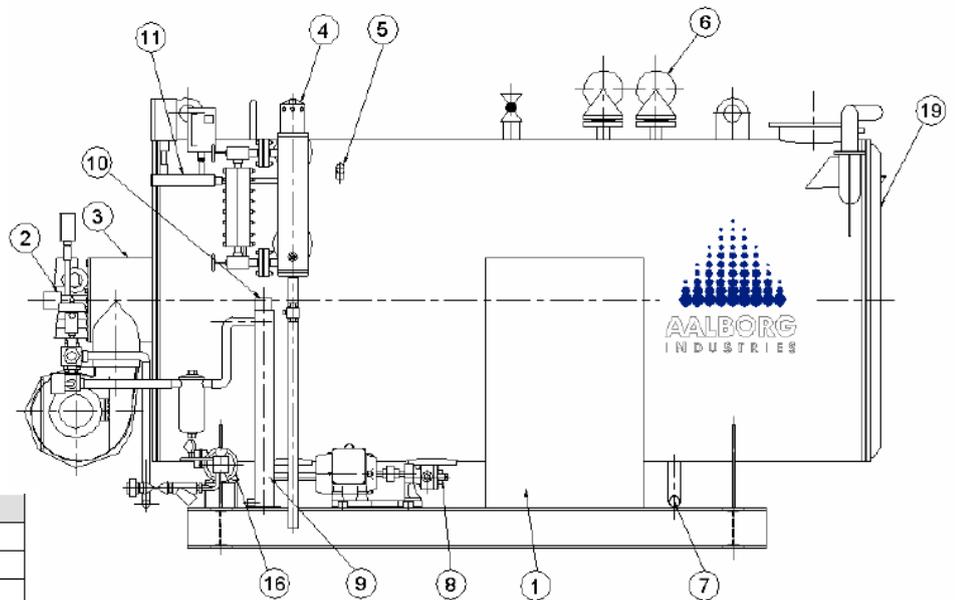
Planta Baixa da Caldeira aguatubular Utilizada na Empresa Vale Verde LTDA.
